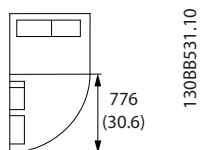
Пространство перед корпусом типа IP21/IP54, типоразмер F8.
